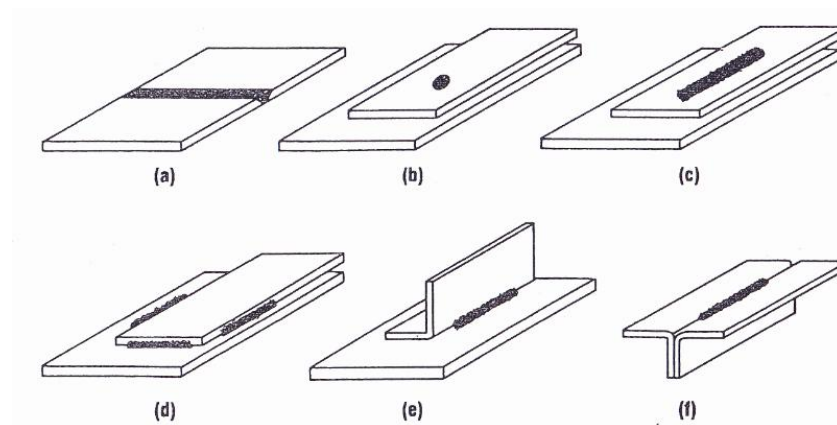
Tipos de soldadura en láminas: (a) de ranura a escuadra, (b) de arco por puntos (soldadura en charco redondo), (c) de arco en costura (soldadura en charco oblongo), (d) de filete, (e) de bisel abocinado, (f) en V abocinada.
